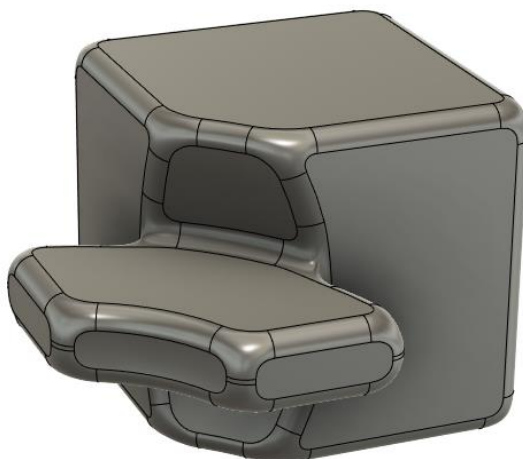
| Elaboración propia | Vista posterior de la pieza de la arista con las esquinas redondeadas
